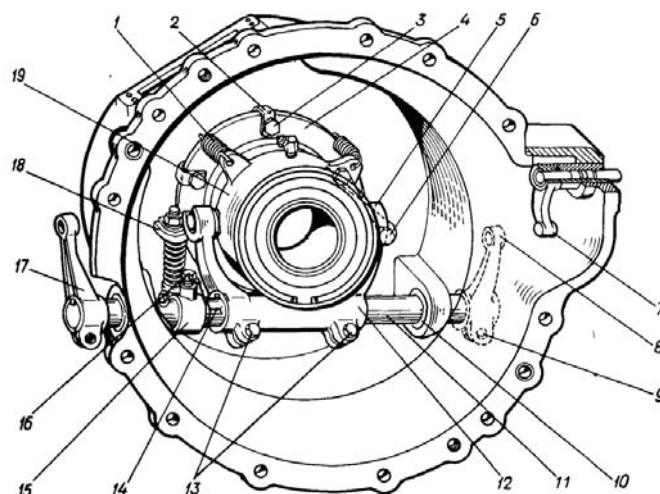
Разборка корпуса: 1 — пружина; 2 — шайба; 3, 6, 9, 13, 16 — болт; 4 — направляющая; 5, 14 — проволока; 7, 8, 17 — рычаг; 10 — втулка; 11 — вал; 12 — вилка; 15 — муфта серги; 18 — колодка тормоза; 19 — корпус выжимного подшипника
